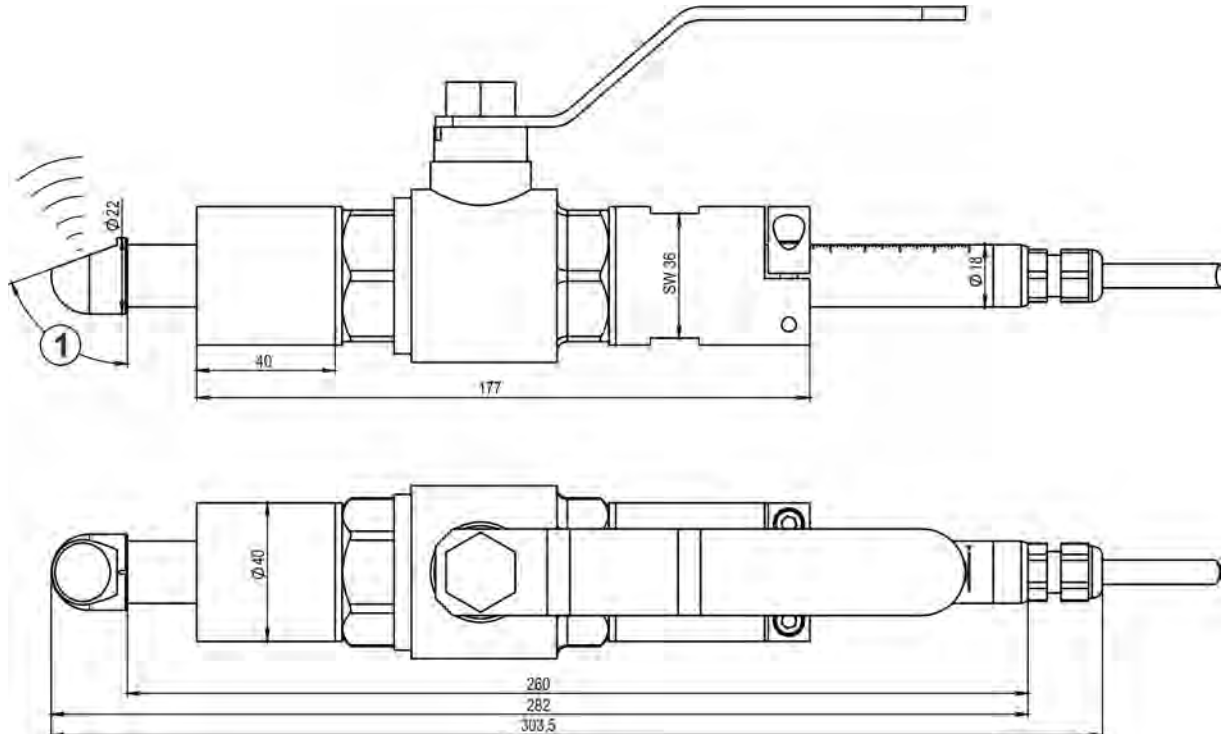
Dimensions du capteur CSM-V1D0K
